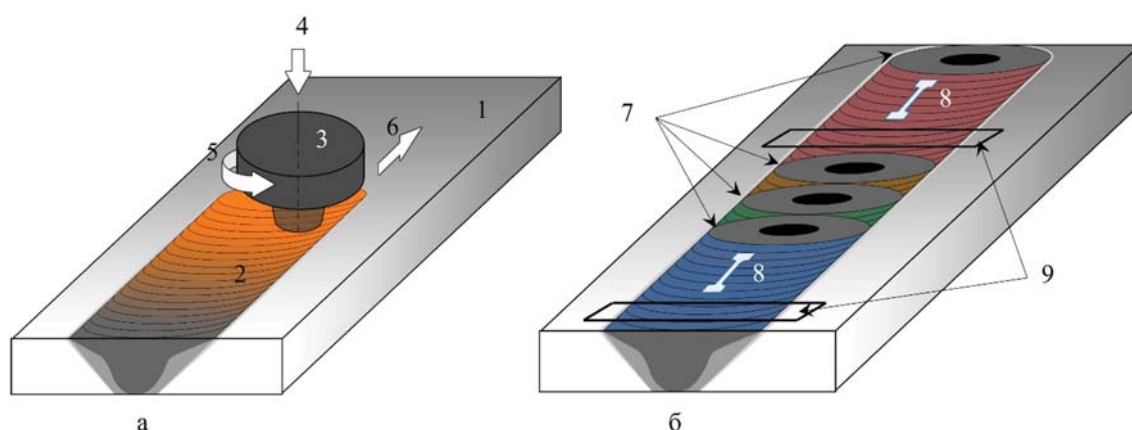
Схема процесса ФПО (а) и вырезки образцов для исследования (б) 1–4 проходов: 1 — заготовка из медного сплава БрАМц9-2; 2 — зона перемешивания; 3 — инструмент для ФПО; 4 — нагрузка на инструмент; 5 — направление вращения инструмента; 6 — направление ФПО; 7 — отверстие от выхода инструмента; 8 — схема вырезки образцов для испытаний на растяжение; 9 — схема вырезки образцов для металлографического исследования
